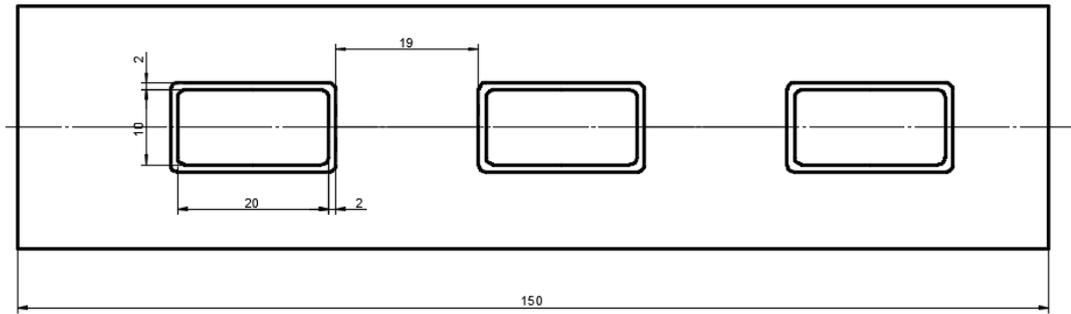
Схема образца для контроля адгезии методом отрыва грибка
